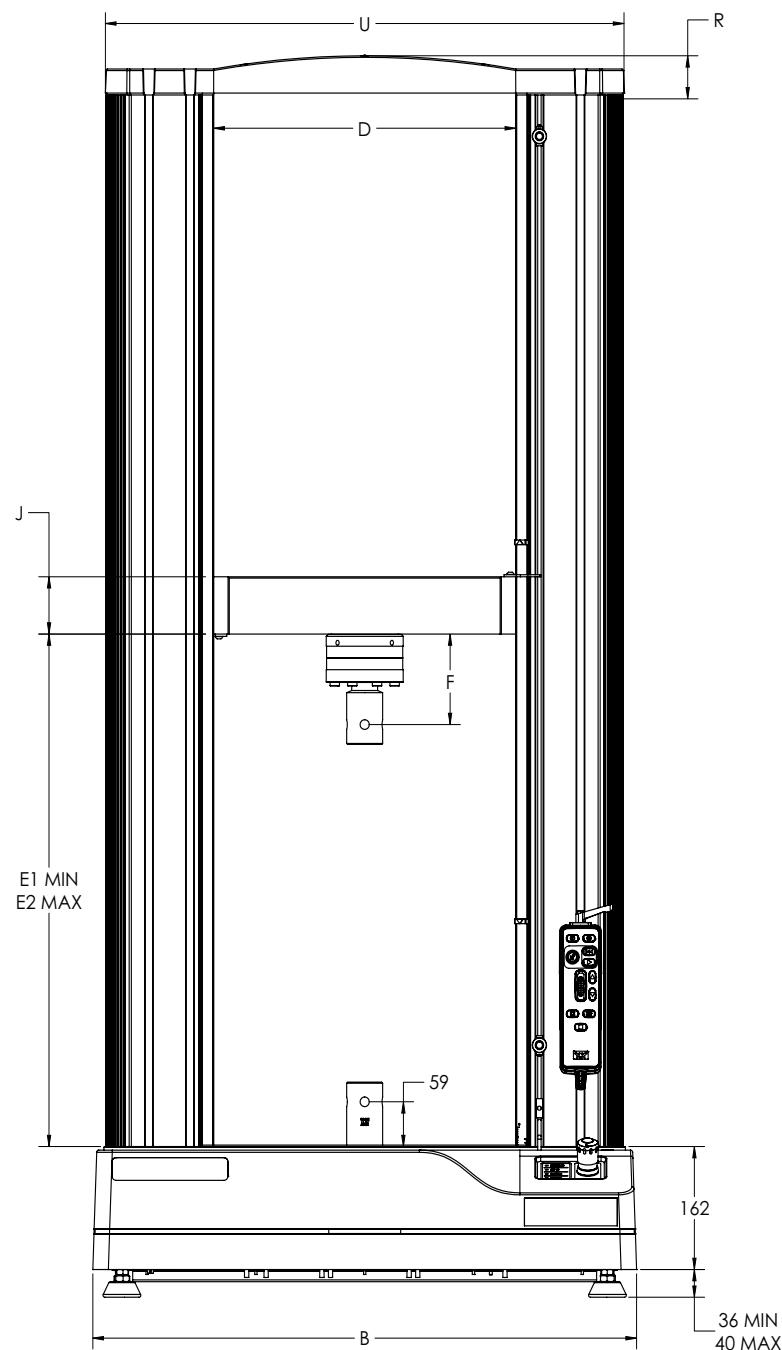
68TM-30 Dimensions du bâti - vue de face
